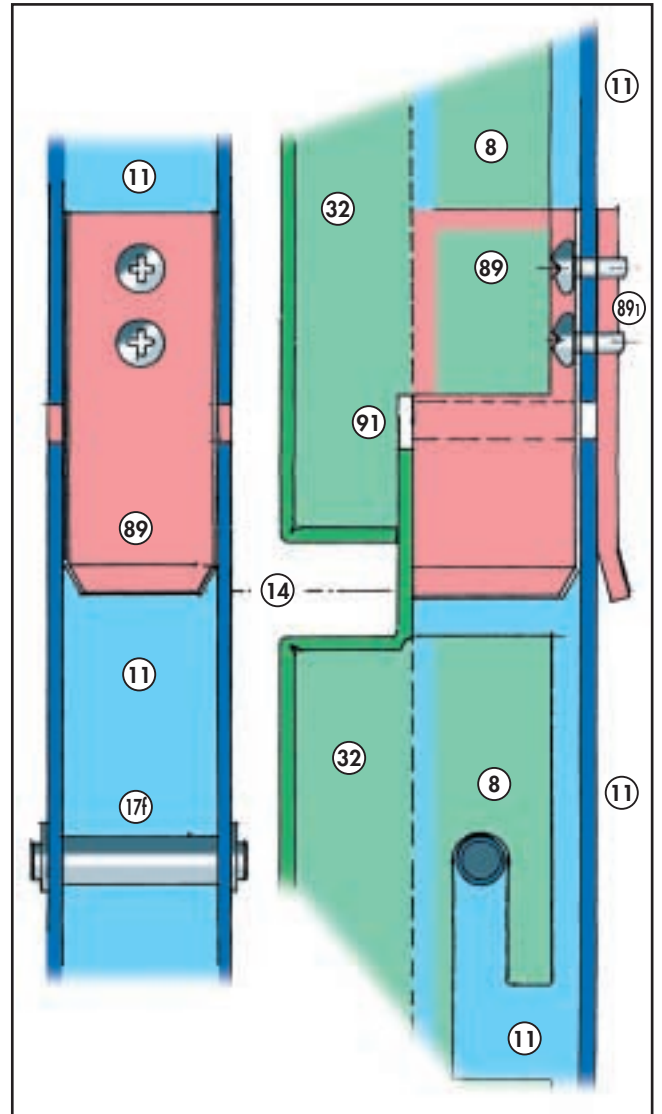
a) - Il giunto (89) che collega gli elementi di montante. Veduta d'insieme
